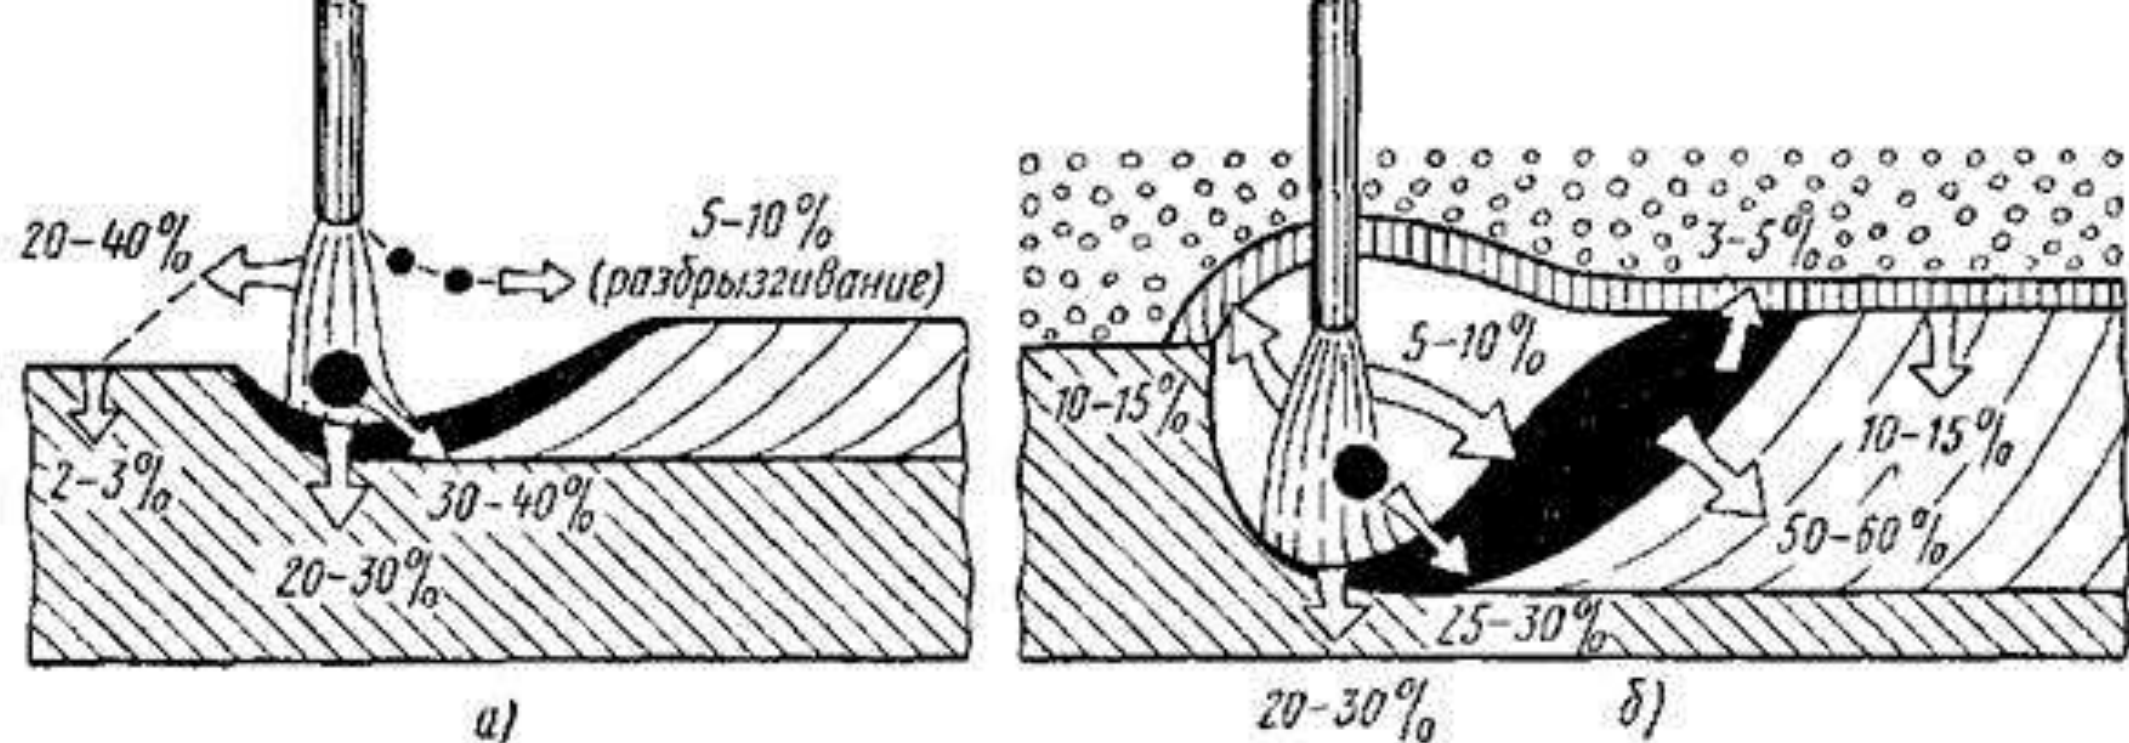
Схема ввода теплоты в изделие сварочной дугой:
